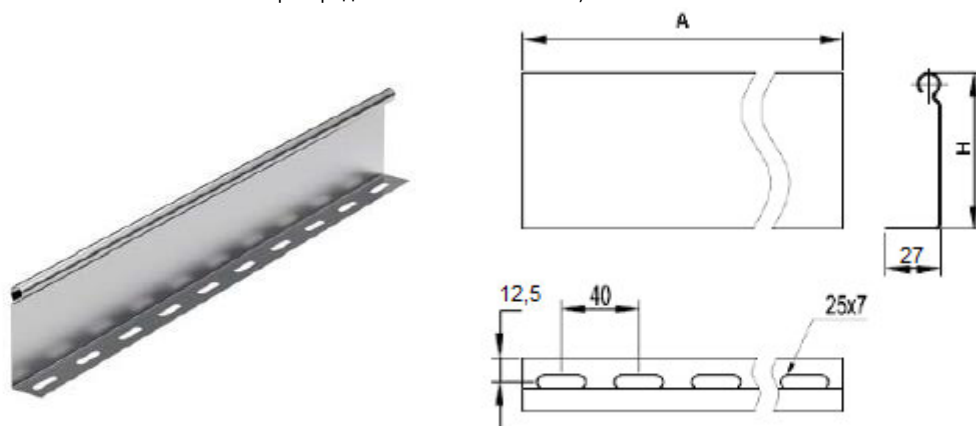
Перегородка SEP, типов: 36460, 36470, 36480, 36490, 36500, 36510, SEP3035
